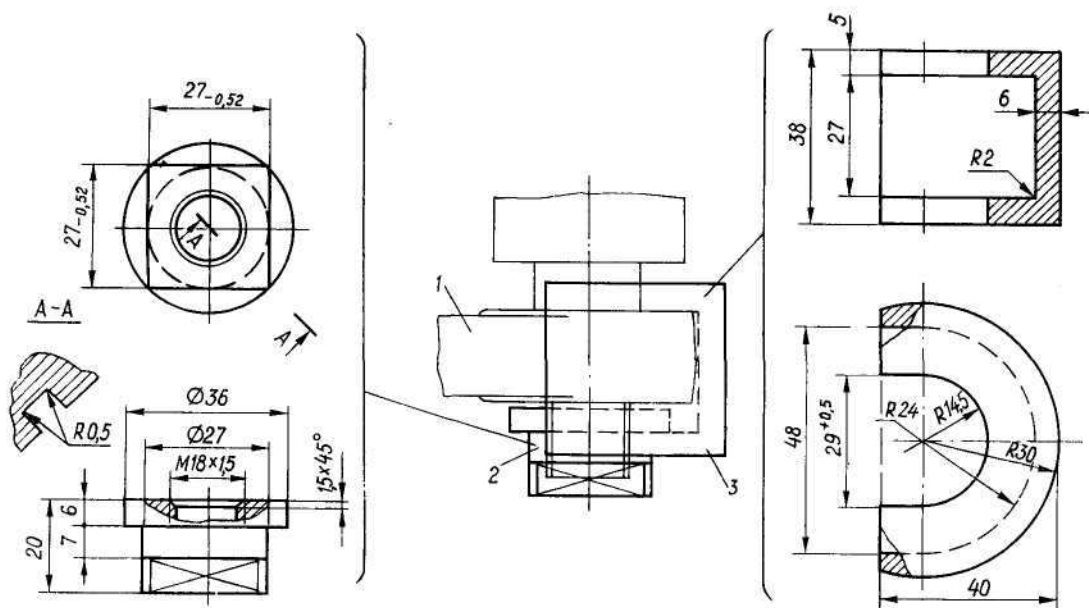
Снятие сошки: 1 — сошка; 2 — гайка съёмника сошки; 3 — корпус съёмника сошки
